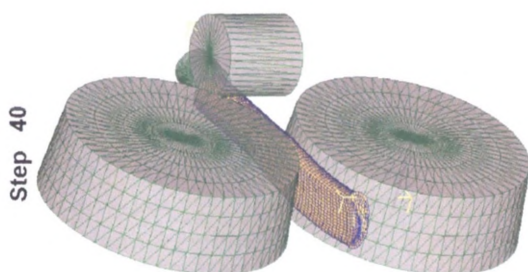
Схема вальцювання криволінійної заготовки
